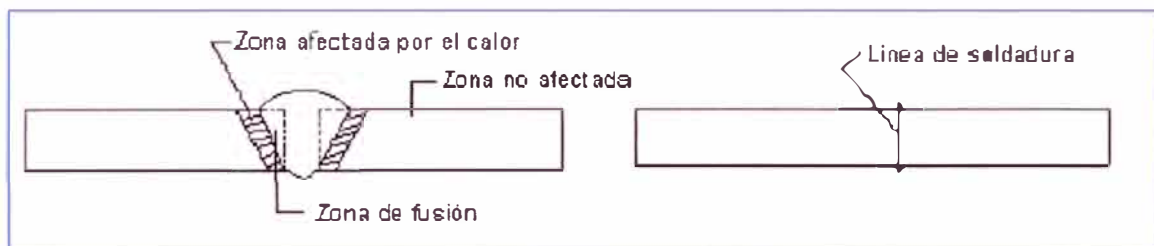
Soldadura por Fusión y Soldadura en Fase Sólida.
